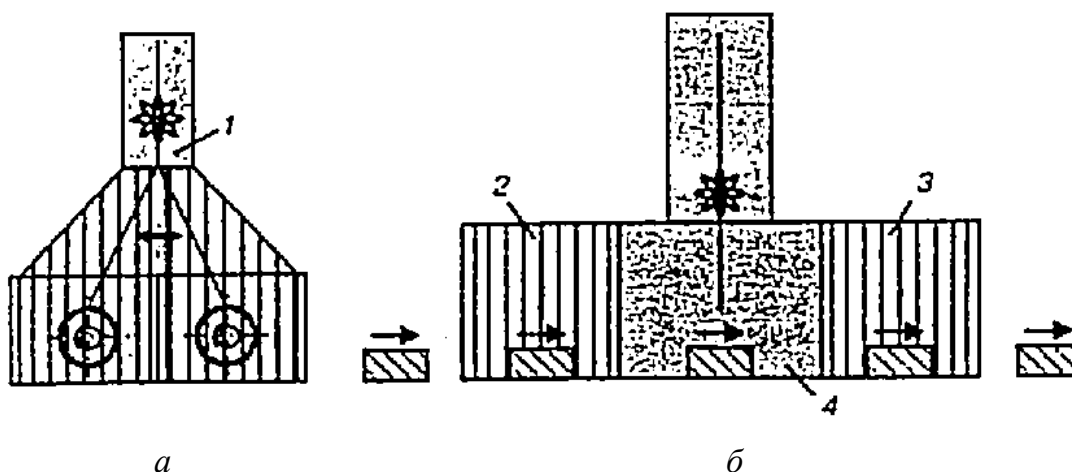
Схемы вакуумных камер для электронно-лучевой сварки:
